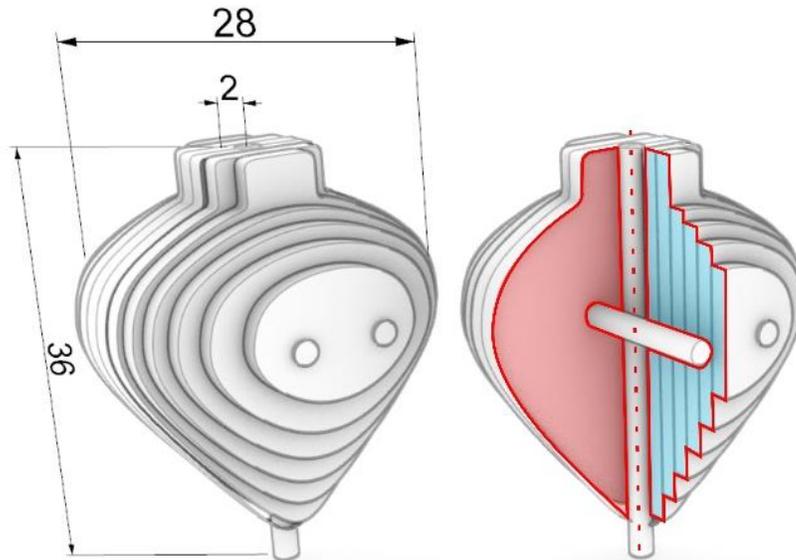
Propuesta de diseño 5, plano seriado con corte paralelo al eje.
